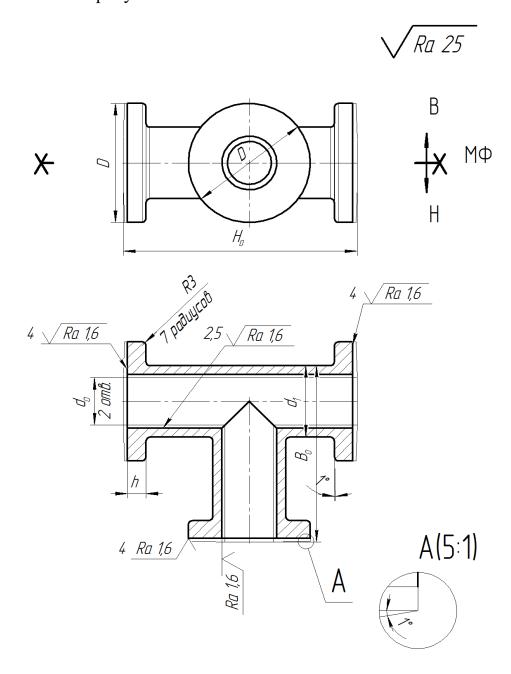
Совмещенный чертёж детали-отливки
